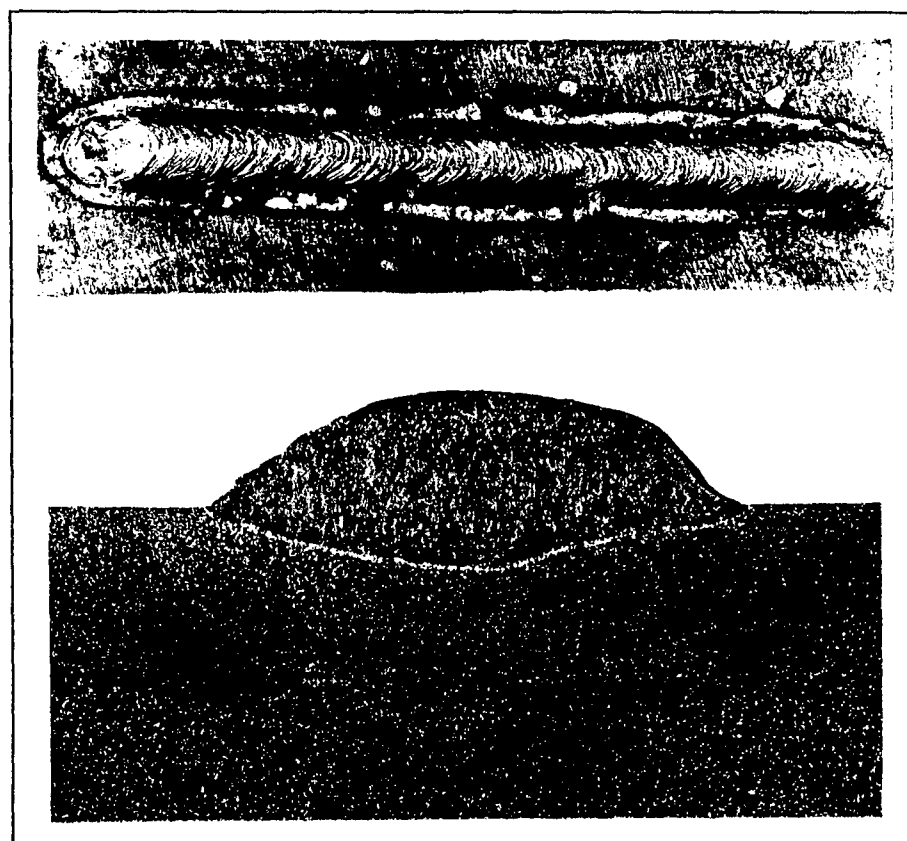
Aspecto do cordão de solda para o eletrodo E em CA.
